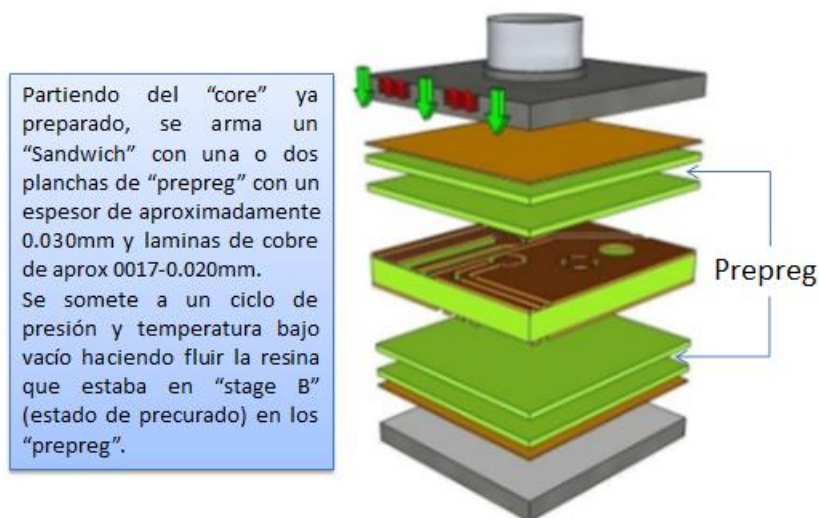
Proceso de fabricación de tableros impresos “ PCB”
